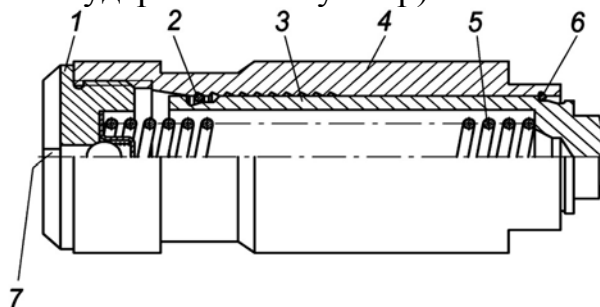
А. Гидронатяжитель 406.1006100-20: 1 – клапан в сборе; 2 - запорное кольцо; 3 - плунжер; 4 - корпус; 5 - пружина; 6 - стопорное кольцо; 7 - отверстие подачи масла
